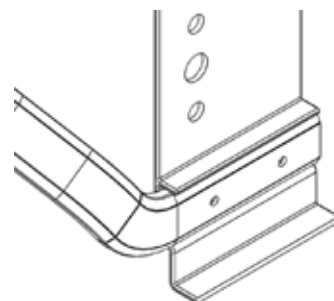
Vista interior da ligação entre o suporte telescópico e a estrutura do canote.
